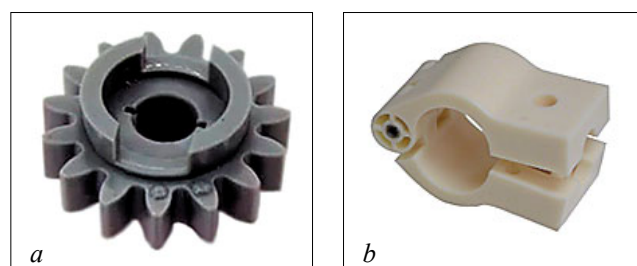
Шестерня привода магнето (а) и опора пальцев шнека жатки *John Deere* (b)
